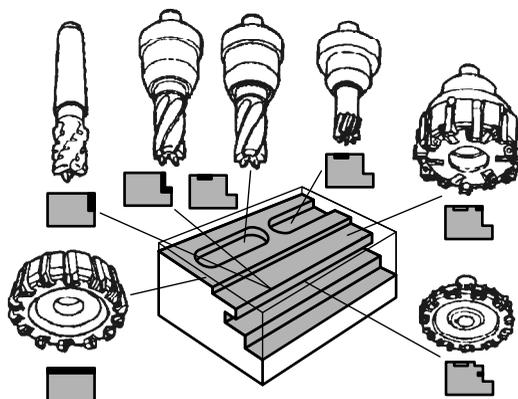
Схема зон и расположения инструментов при фрезерной обработке детали
